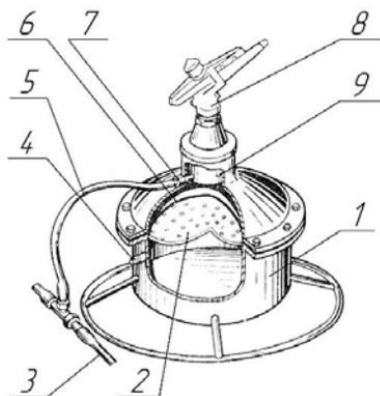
Импульсный дождеватель: 1 – гидроаккумулятор; 2 – свод; 3 – поливной трубопровод; 4 – штуцер для заполнения гидроаккумулятора воздухом; 5 – шланг; 6 – эластичная мембрана; 7 – присоединительный штуцер; 8 – дождевательный аппарат; 9 – запорный орган.
